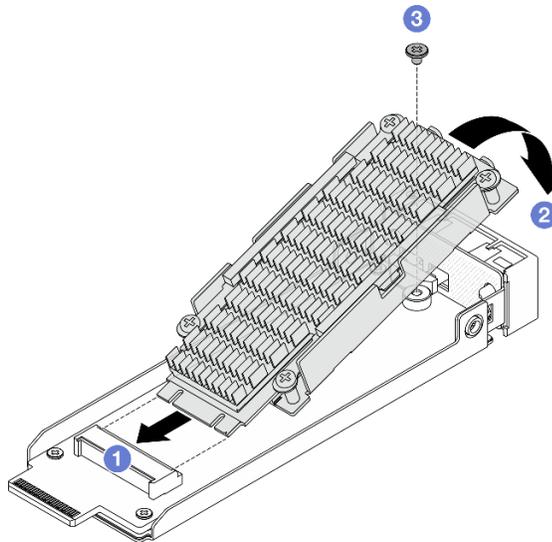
Assemblage de l'adaptateur M.2 et de l'unité
